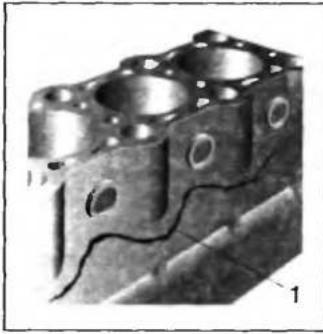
Схема образования трещины (1) по приливам резьбовых отверстий на блоке
